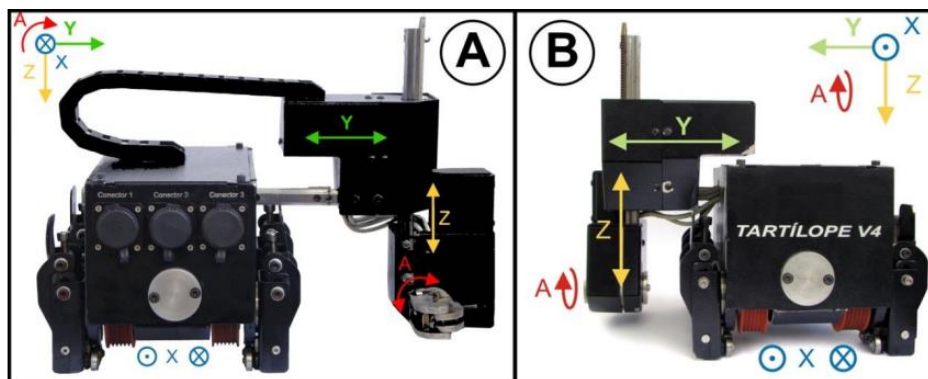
Representação das juntas do Tartilope v4 no (a) arranjo para soldagem de tubos e (b) arranjo para soldagem de dutos [Fonte: SPS, 2013].
